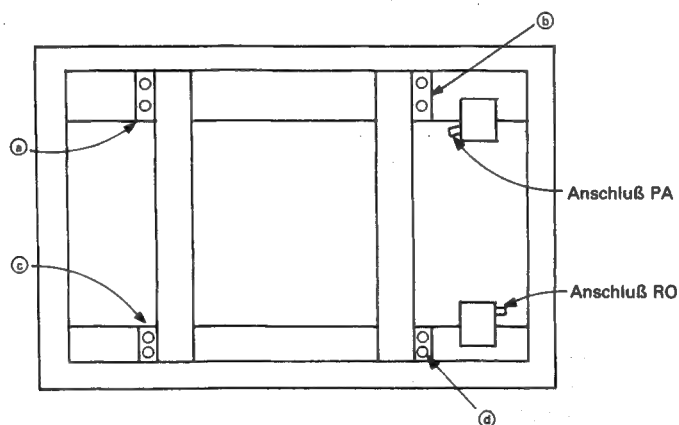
Drehmechanismuseinheit mit entfernter Rückwand
